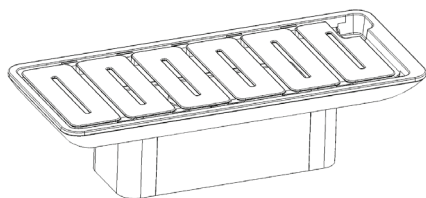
MONTAGE DER PLATTEN AUS CORIAN
